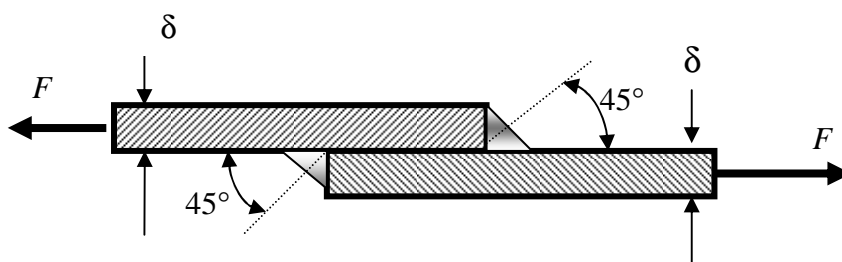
Схема нагружения лобового сварного шва
